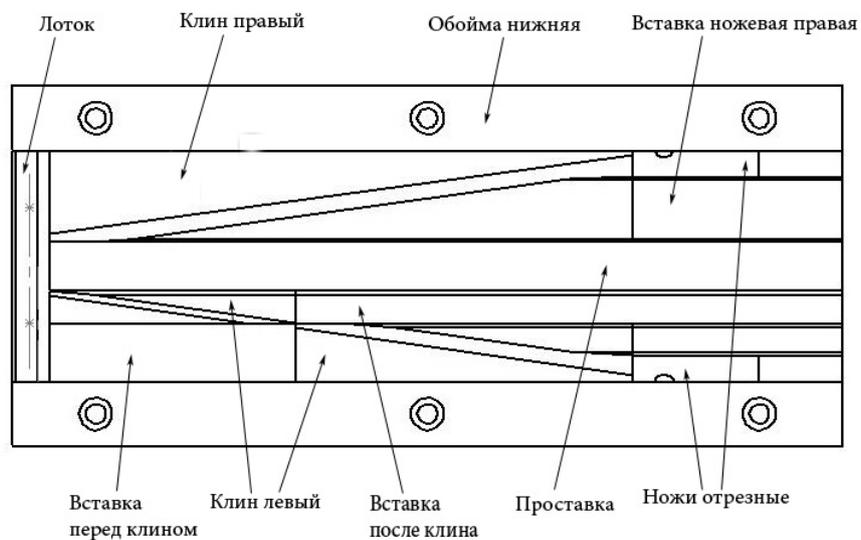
Схема расположения элементов инструмента в сборочной модели
